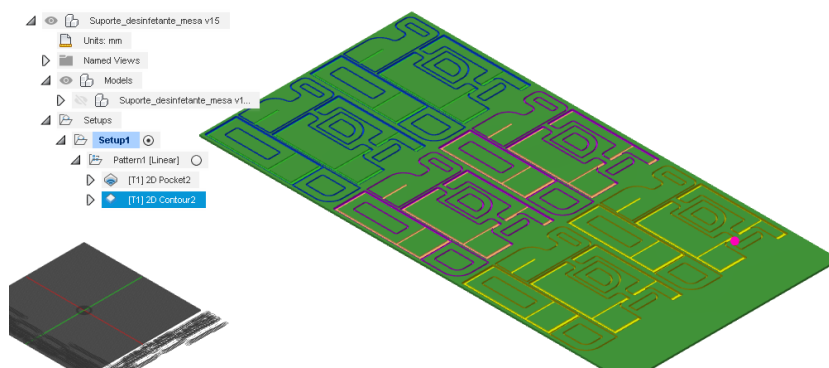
Maquinação para a fresadora CNC do suporte do desinfetante e papéis
